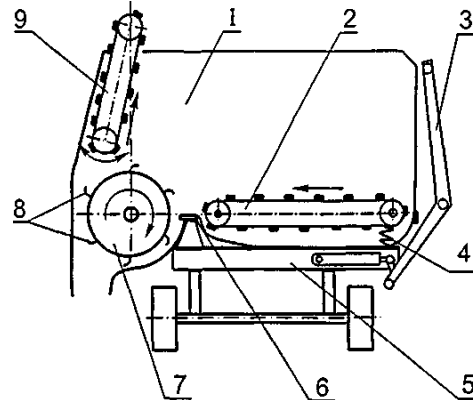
Конструктивно-технологическая схема измельчителя-раздатчика грубых кормов:
